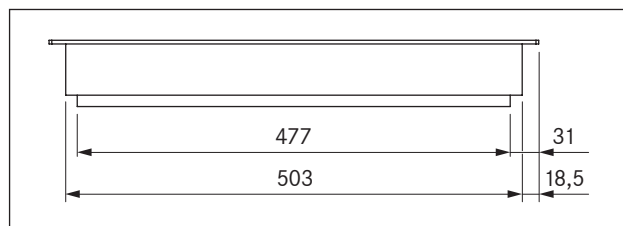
PKT11 dimensioni apparecchio vista laterale
